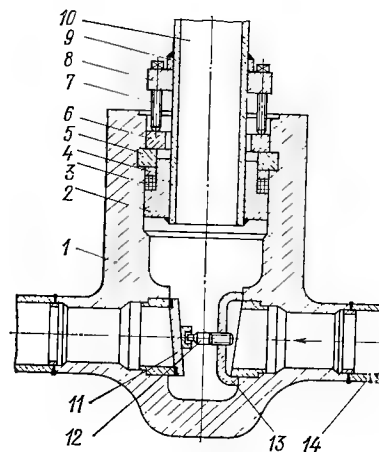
Установка заглушки и выпускного патрубка на паровой задвижке.
